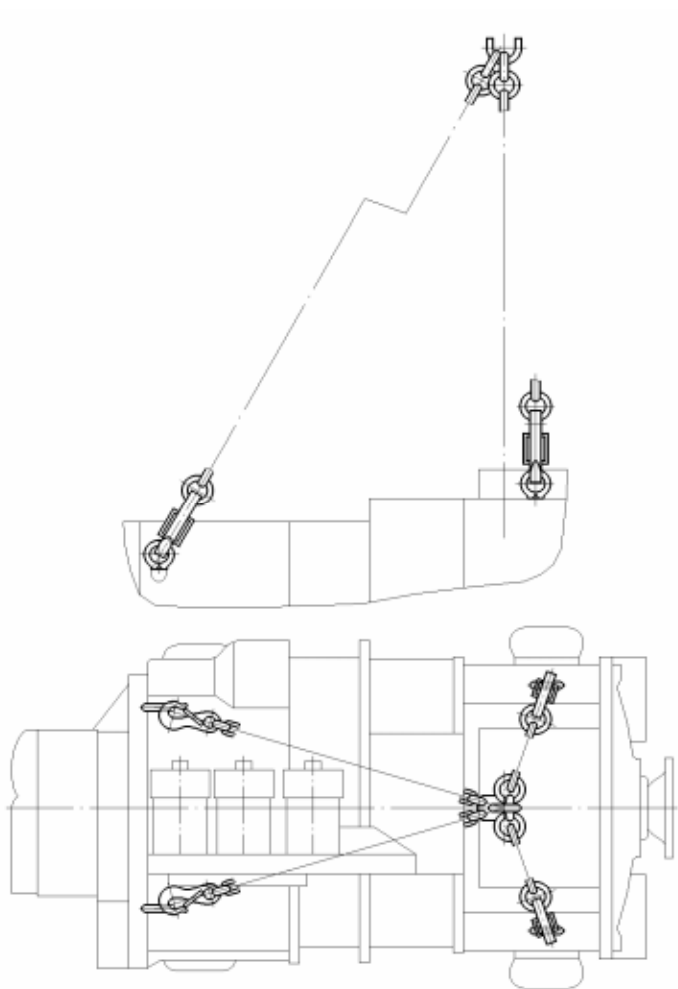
Приспособление для снятия и установки гидромеханической передачи
